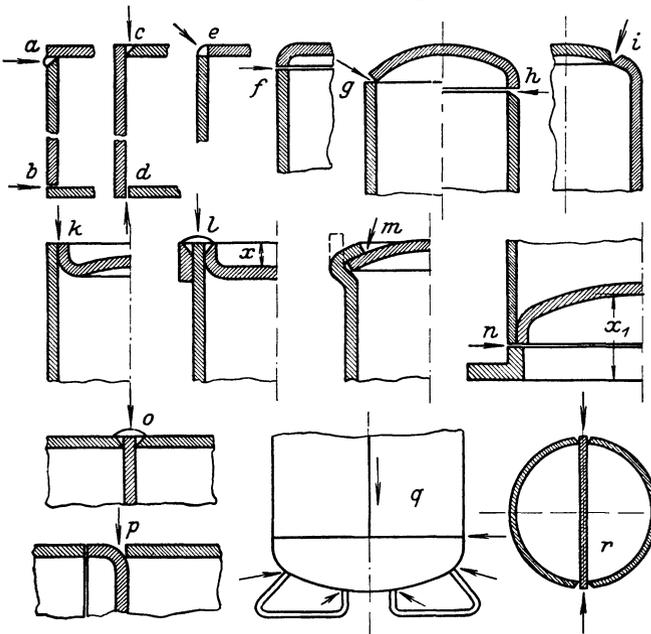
Schweißung von Blechböden und Zwischenwänden.
